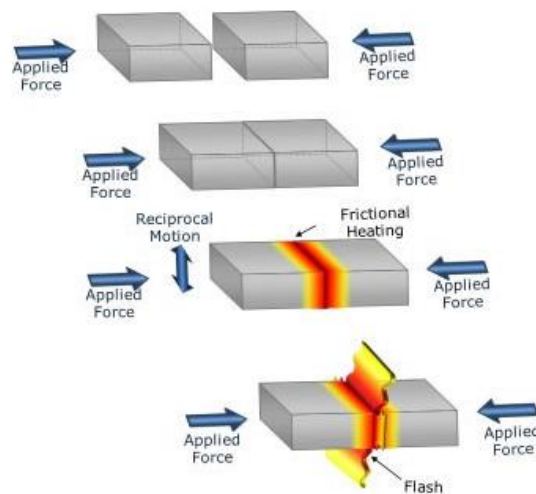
Proceso de soldadura por fricción lineal [2]
